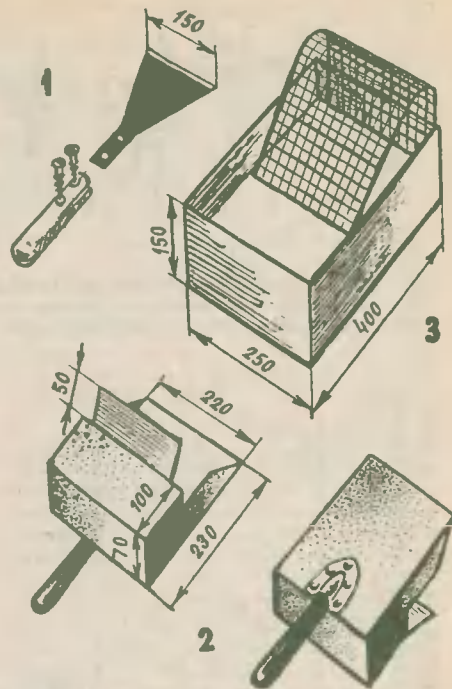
Шпатель (1) и скребок (2) из металлического листа — для зачистки старых покрытий потолка и стен; ваиночка (3) — для красящих составов.
